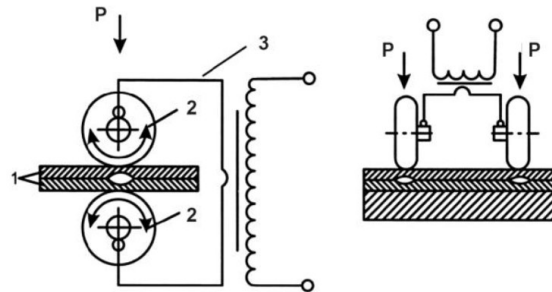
Схема шовного зварювання і розріз зварного шва:
